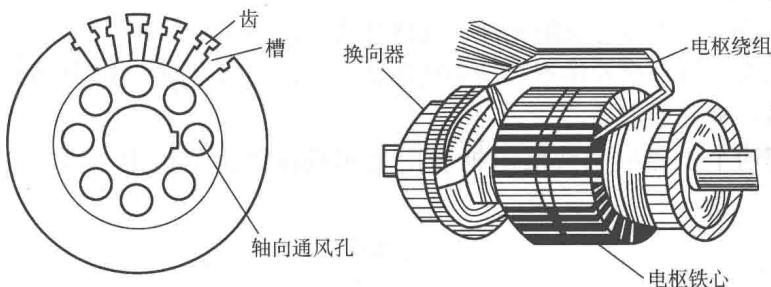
小型直流电机的电枢冲片形状和电枢铁心装配图
